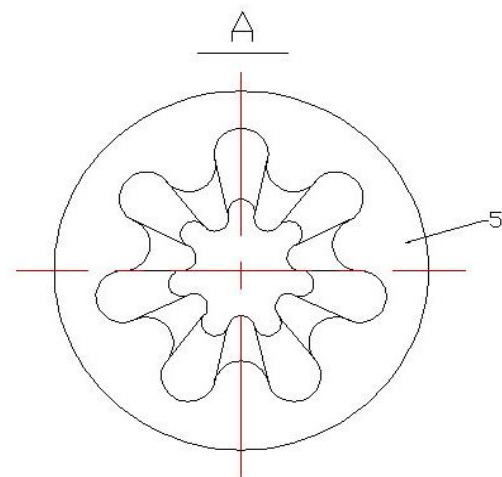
Кольцевой центральный блок, вид по стрелке А
